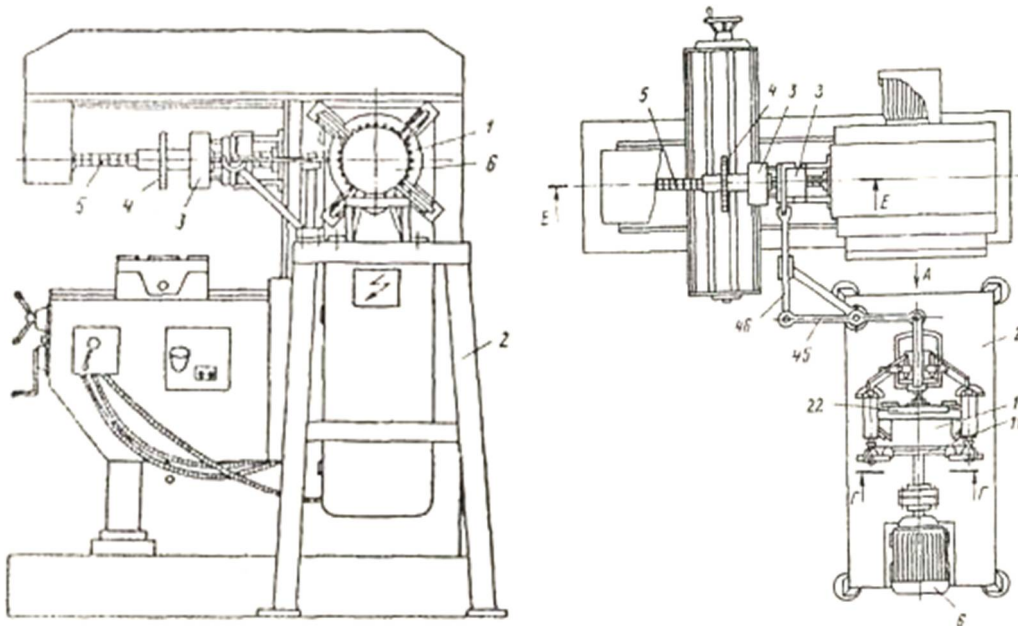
Загальний вигляд фрезерного верстата із приводом шпинделя вібраційного різання [40]
